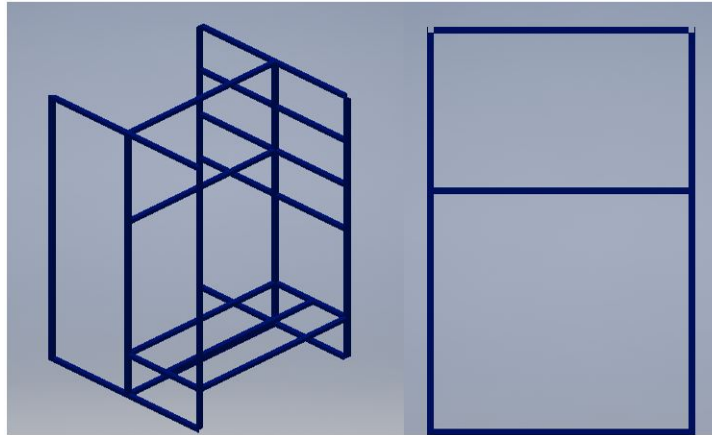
Base para montaje de compresor correspondiente a la sección 1 del sistema de refrigeración
